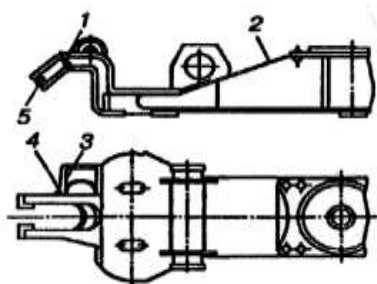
Дефекти надресорних балок візків КВН-ЦНП: 1 - злам кронштейна; 2 - тріщина в зварному шві; 3, 4 - тріщини в зварному шві з'єднання опорної плити з кронштейнами відповідно повідка і гідрогасника; 5 - знос втулки
